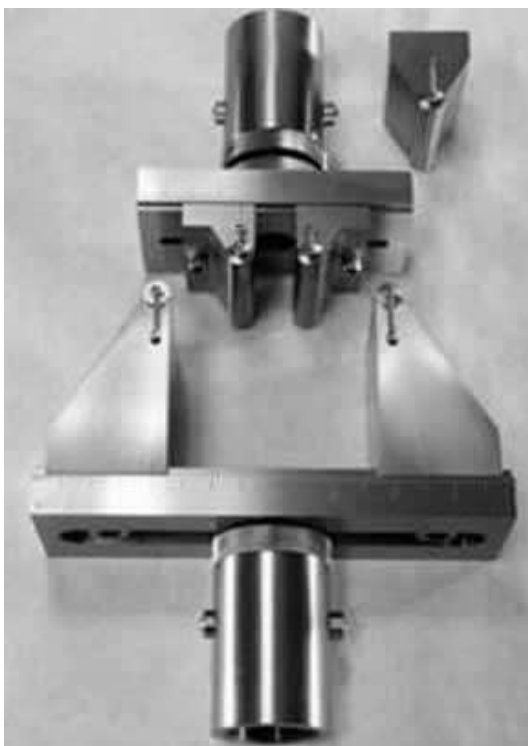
Přípravek pro tříbodovou ohybovou zkoušku dle ASTM D790-15 [17].
